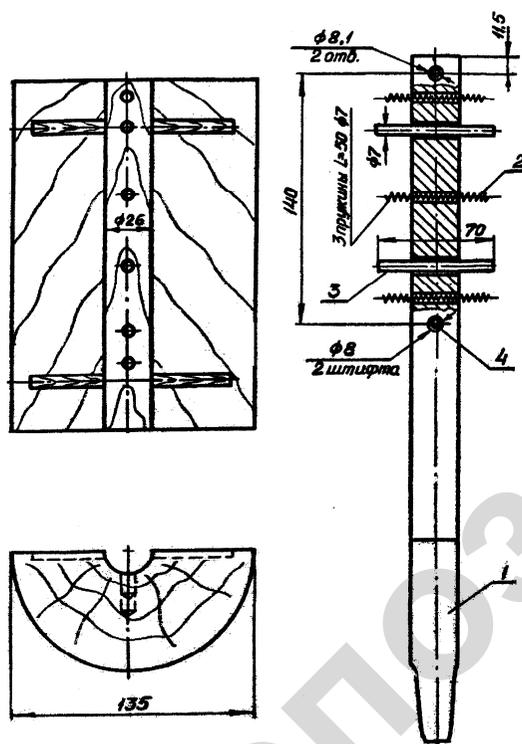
Приспособление для шлифовки цилиндра насоса:
